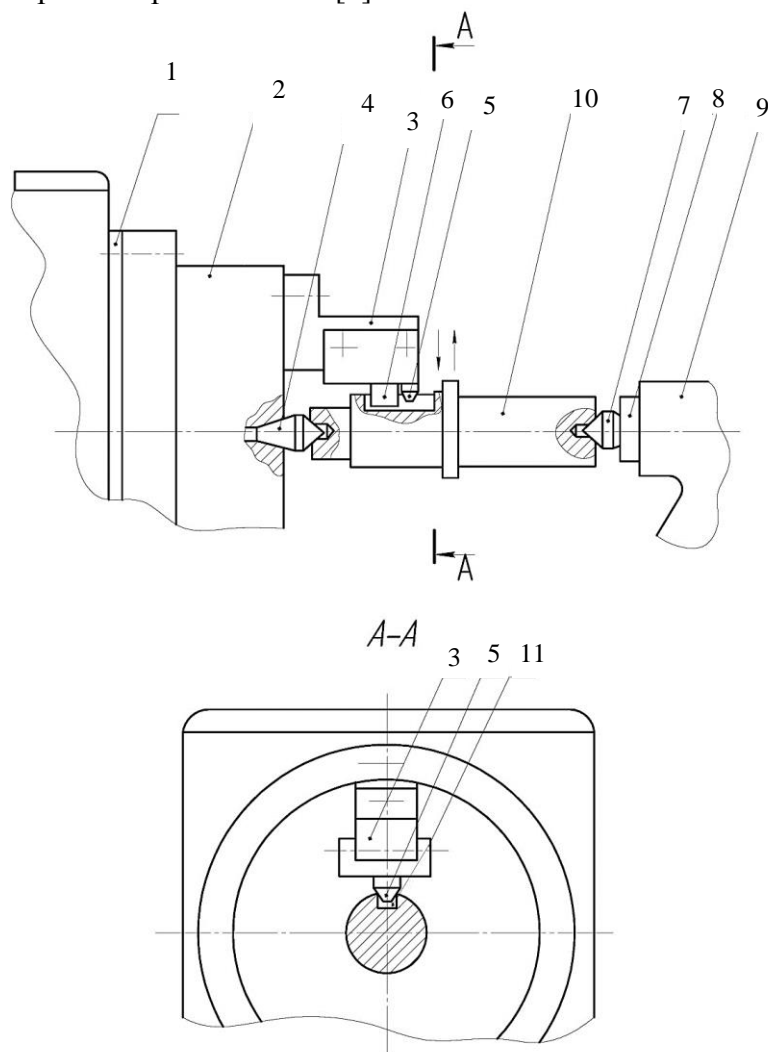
Схема способа установки вала со шпоночным пазом на центрах станка
